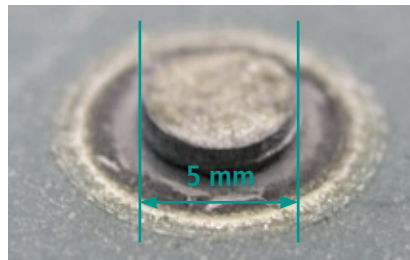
Durch Kopfzug erzeugter Butzen einer Probeschweißung
